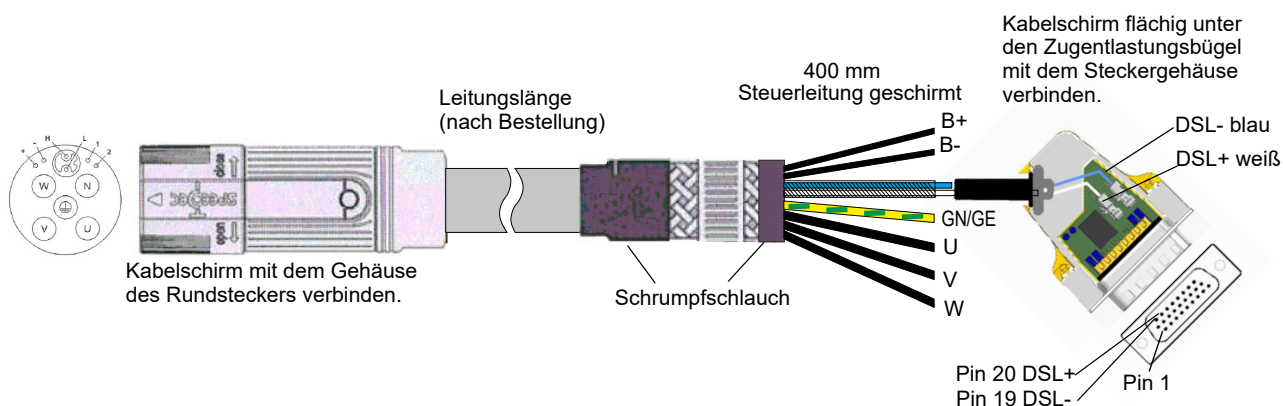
Motorleitung mit HIPERFACE DSL® 28 A
